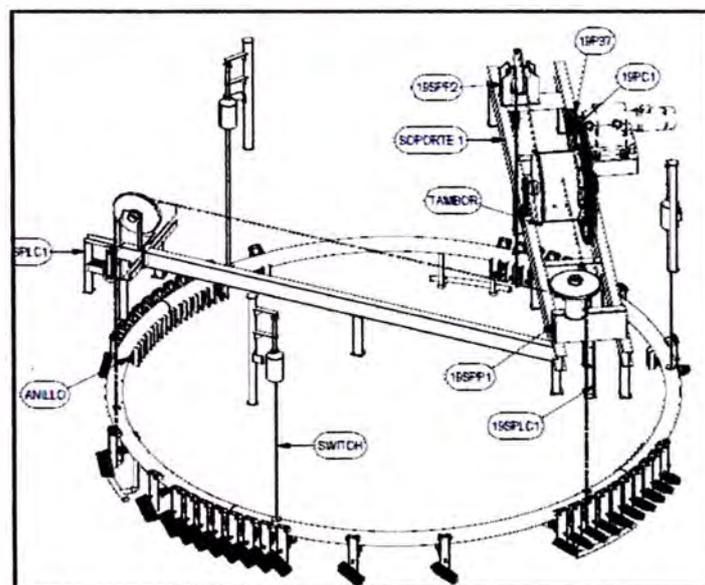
Sistema de limpieza del Cuerpo de la Torre
